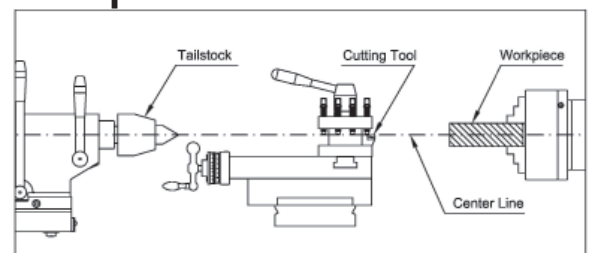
Outil de coupe aligné avec le centre de la pièce à usiner
